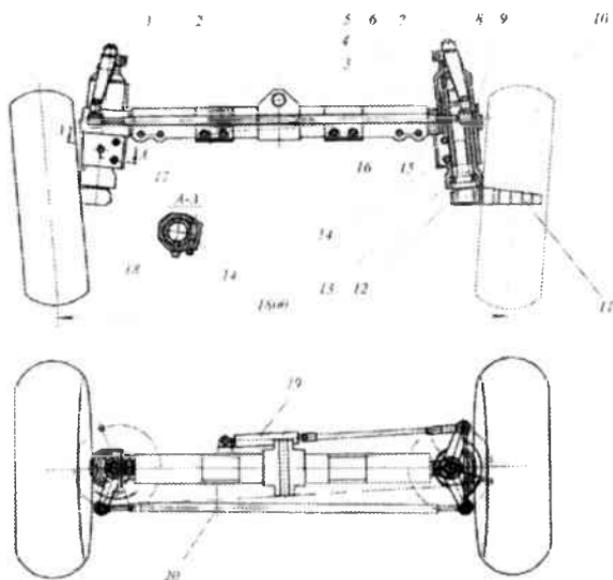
Передний мост с регулируемым клиренсом: 1 – рычаг; 2 – ушко; 3- шлицевая труба; 4 – шлицевой вал; 5 - выдвижная труба колени; 6 – полая труба; 7 – кронштейн шлицевой трубы; 8 – двуплечий рычаг; 9 – кронштейн; 10 – колесо; 11 – полуось; 12 – цапфа; 13 - подшипник; 14 – фиксатор; 15 – выдвижная труба балки; 16 – фиксирующие болты; 17 – балка; 18 – стопорный болт; 19 – гидроцилиндр; 20 – тяга
